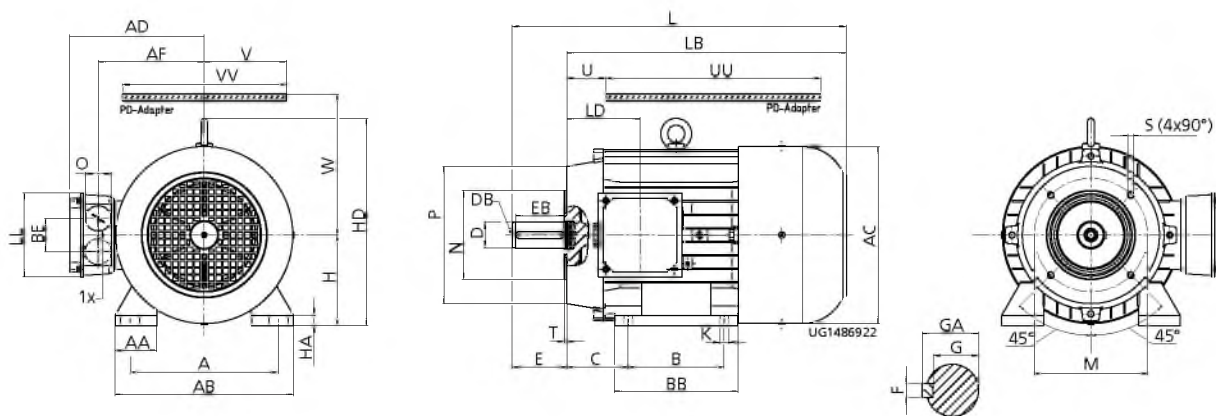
Двигатель с клеммной коробкой и фланцем FT с резьбовыми отверстиями (V18,...)
